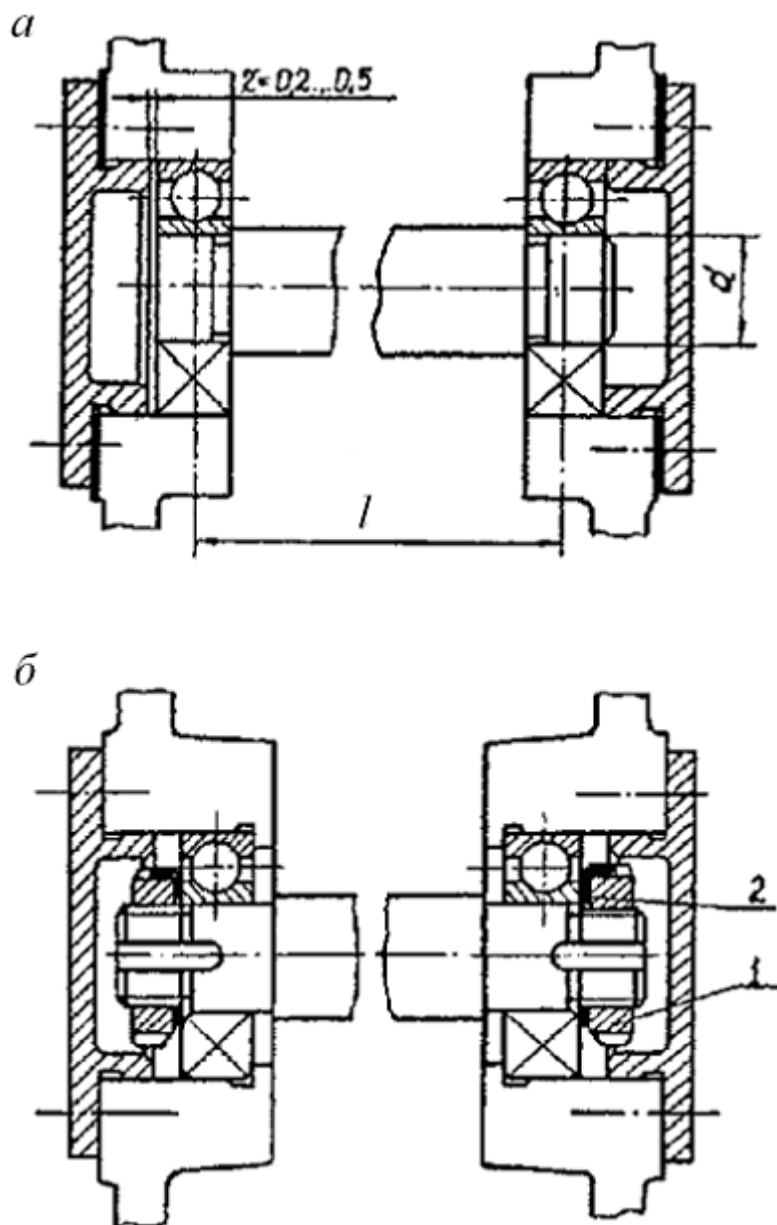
Установка вала на двух фиксирующих опорах. а) схема «враспор»; б) схема «врастяжку». 1 — круглая шлицевая гайка; 2 — многолапчатая шайба.
